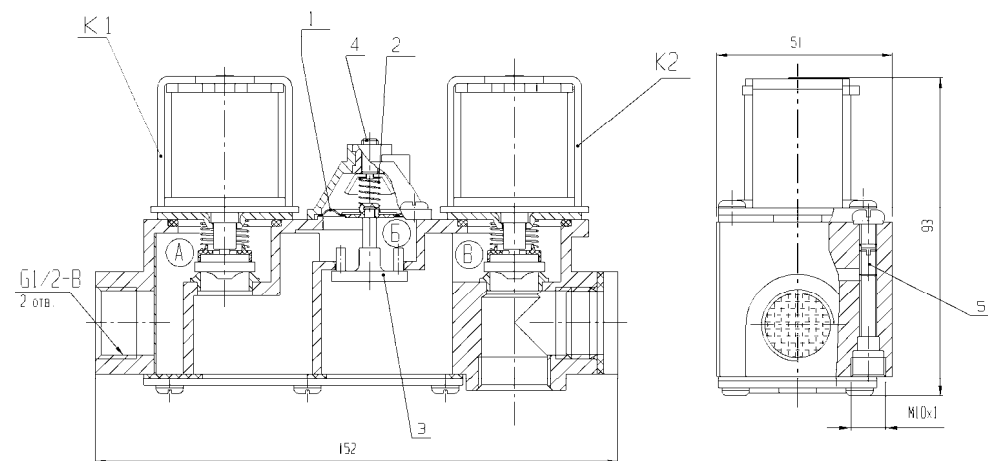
Устройство, габаритные и присоединительные размеры блока клапанов автоматики САБК-Э
